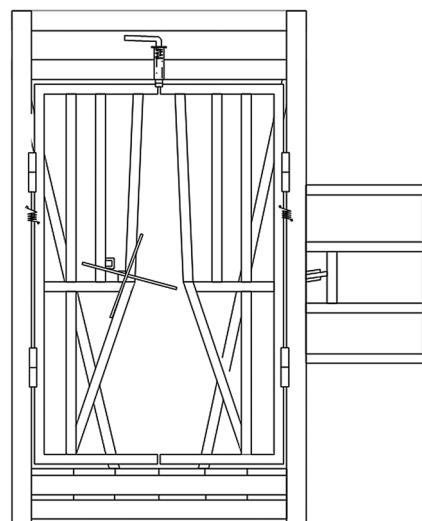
Поворотный станок для искусственного осеменения овец, вид спереди
